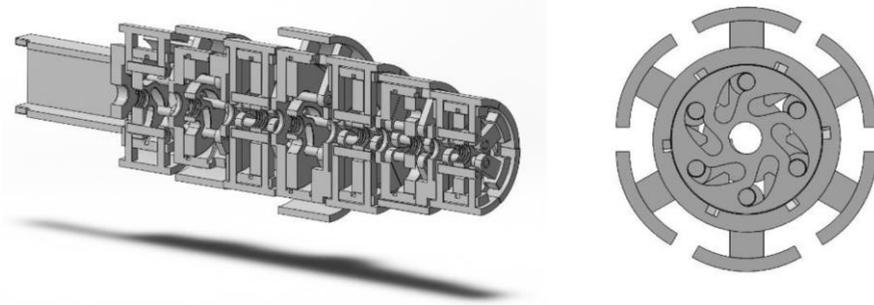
Prinzip der Mikromotorik im Längsschnitt (links) und Querschnitt (rechts)
